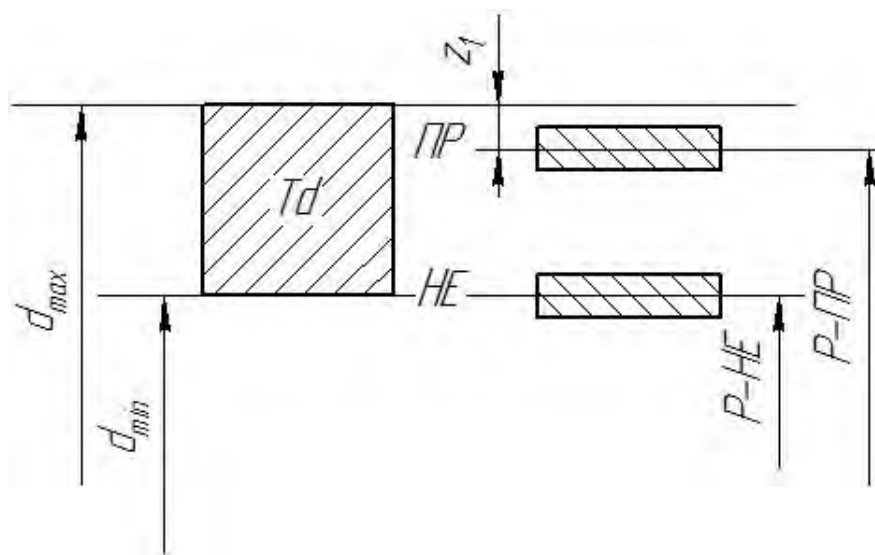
Схема расположения интервалов допусков калибров-скоб (до 180 мм)
